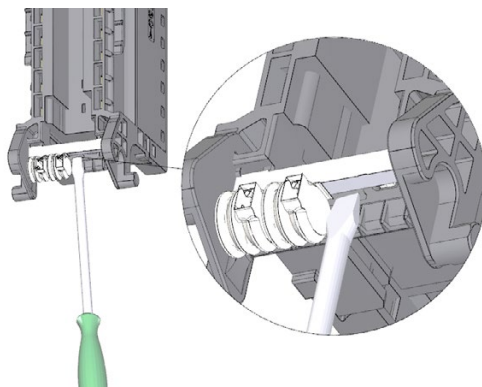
Mechanisches Kodierelement aus dem Frontstecker entfernen
